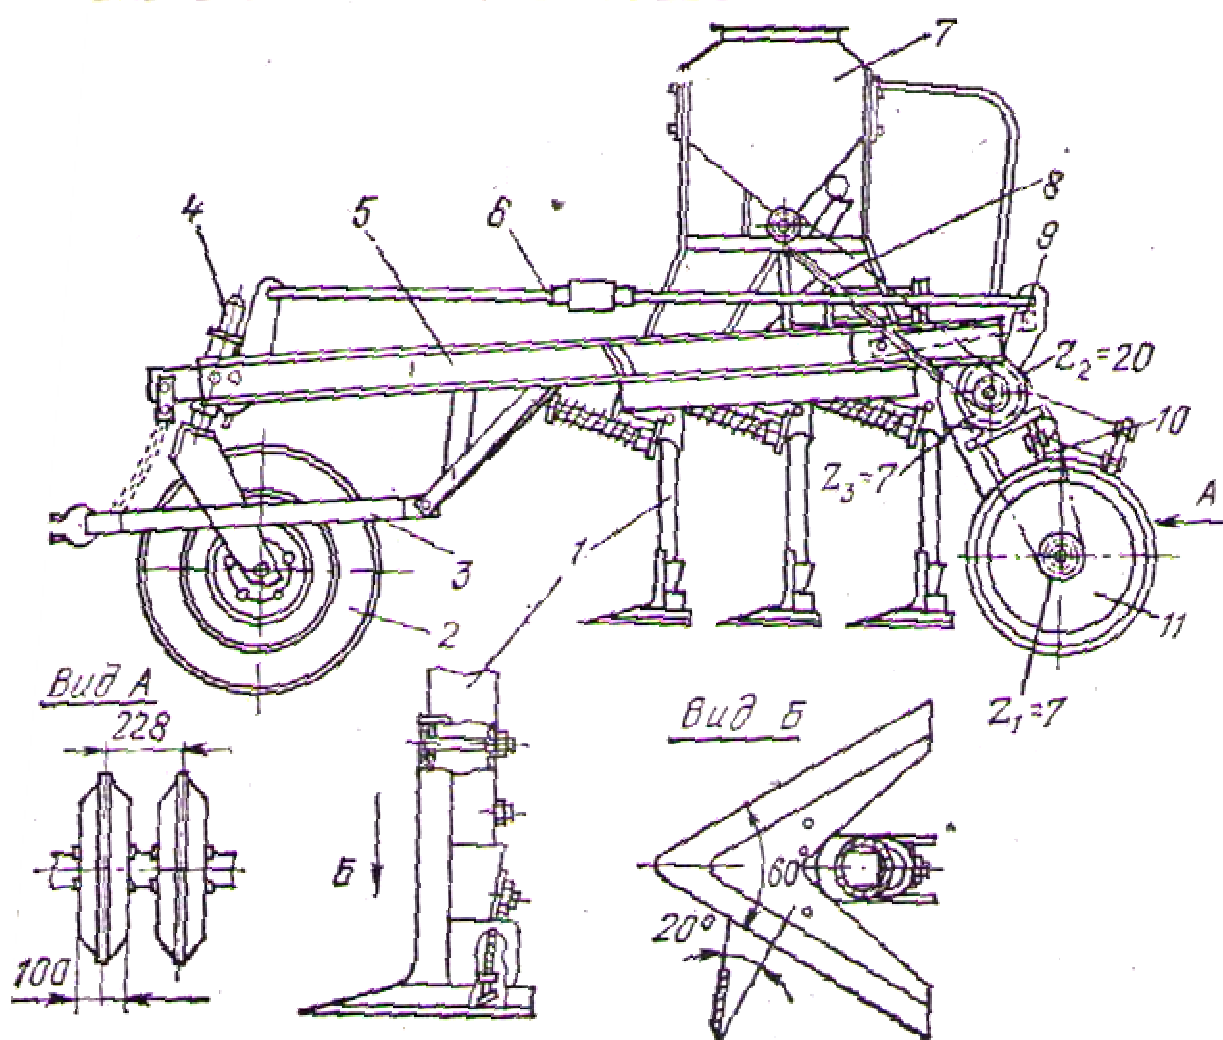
Сеялка СЗС-2,1: 1 - сошник; 2 - колесо опорное; 3 - устройство прицепное; 4 - ось вилки опорного колеса; 5 - рама; 6 - тяга длинная; 7 - ящик зернотуковый; 8 - устройство гидравлическое; 9 - планка транспортная; 10 - кронштейн; 11 - прикатывающие катки.
